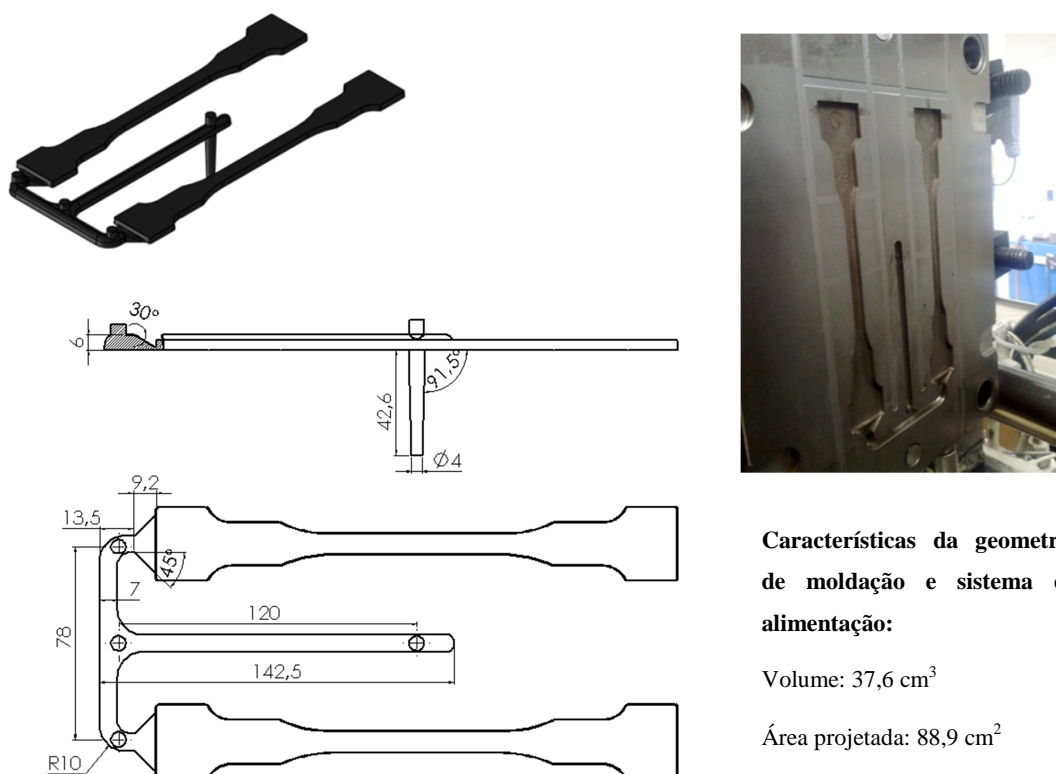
Geometria de moldação, sistema de alimentação e molde de injeção.
